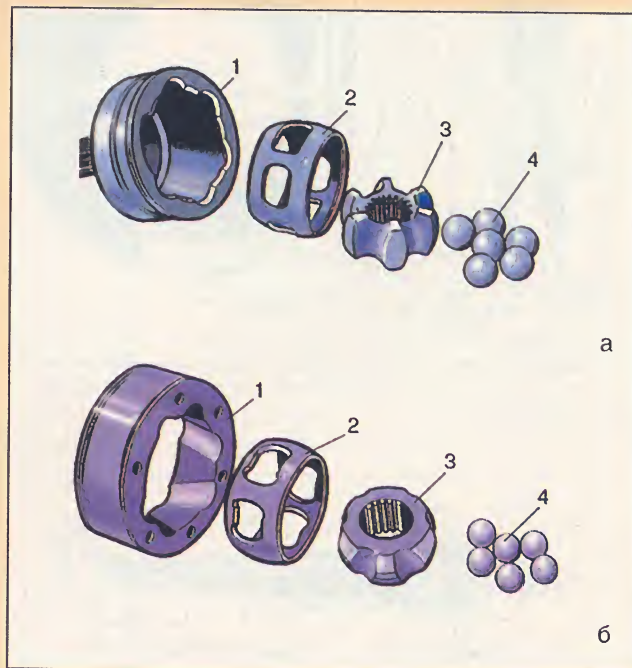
Детали наружного (а) и внутреннего (б) шарниров: 1 - корпус шарнира; 2 - сепаратор; 3 - обойма; 4 - шарик.
